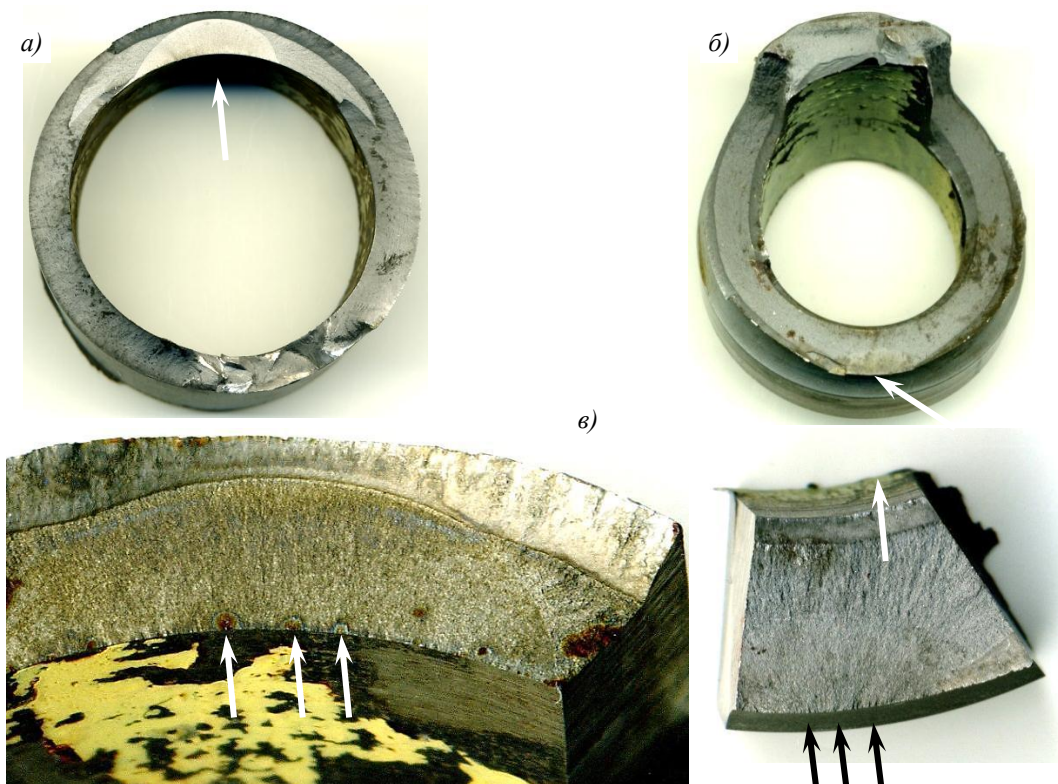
Макростроение излома рессоры: *а* – первичная трещина; *б* – вскрытая вторичная трещина; *в* – вид излома, образованного первичной трещиной. Стрелками отмечены очаги разрушения
